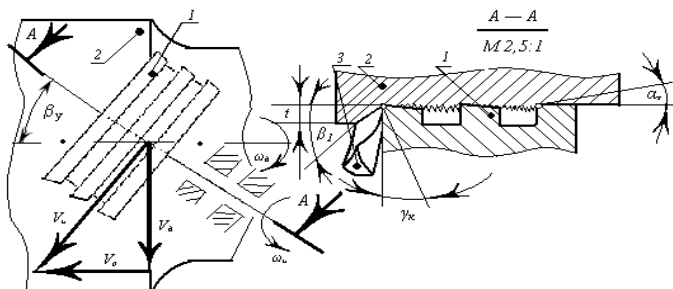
Многозевый ротационный резец для точения тел вращения: 1- режущие элементы; 2 - обрабатываемая деталь; 3 - отделяющаяся стружка; β_y - угол установки режущих элементов; β_1 - угол сдвига срезаемого слоя; α_k - кинематический задний угол режущего элемента; γ_k - кинематический передний угол режущего элемента; ω_d , ω_n - угловая скорость детали и режущих элементов соответственно; V_d , V_n - линейная скорость детали; и режущих элементов соответственно; V_p - скорость резания
